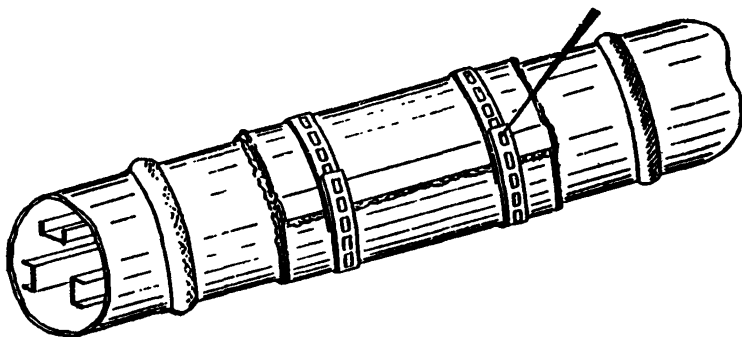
Приспособление для обжатия полуцилиндров перед приваркой их к оболочке
